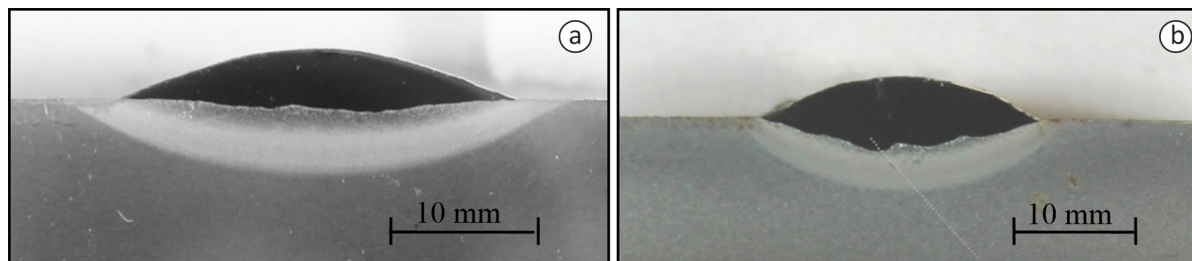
Macrografia de um cordão de solda (a), com Ar + 25%He e (b) soldado com Ar+ 4%CO₂.
